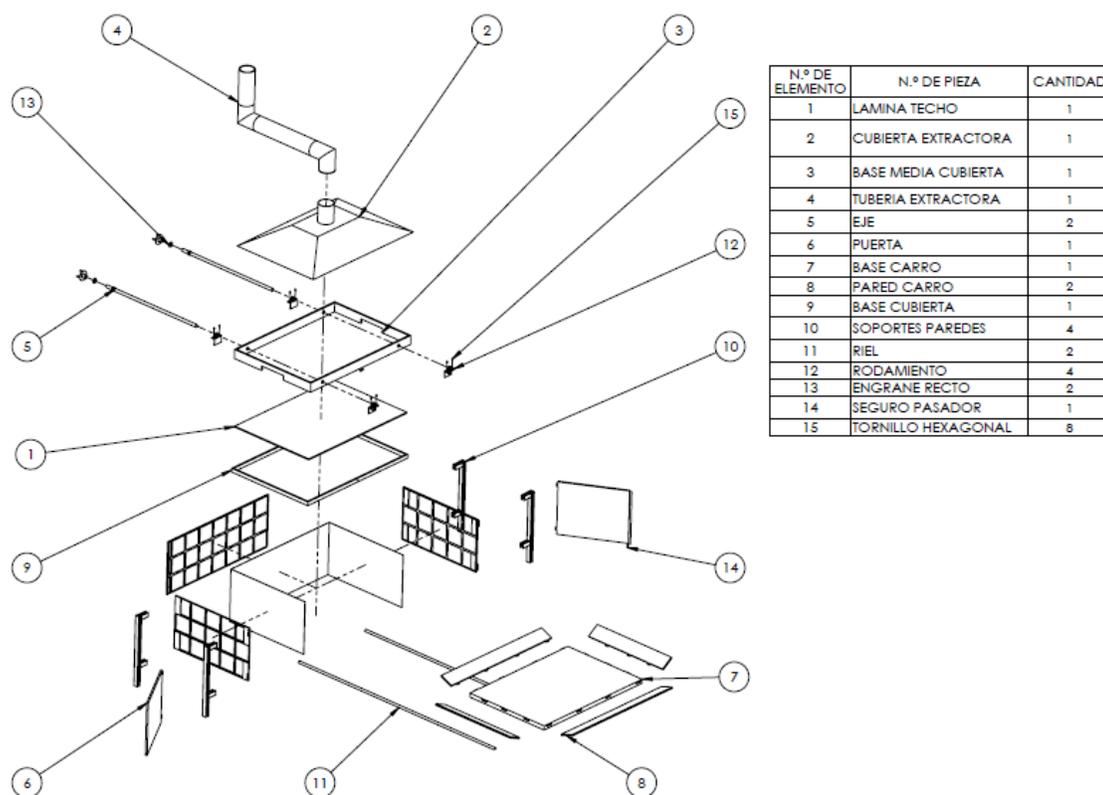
Despiece del Diseño del Molde Rectangular de Espuma
